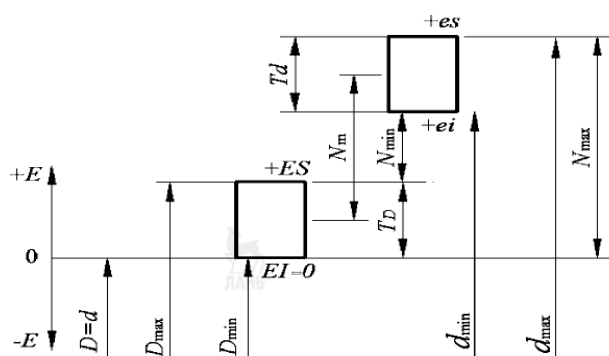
Схема расположения интервалов допусков посадки с натягом
